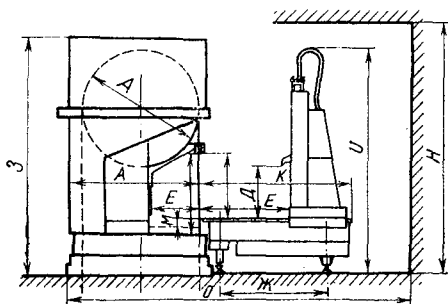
Схема ленточнопильного станка с кареткой (обозначения см. табл. 6)
